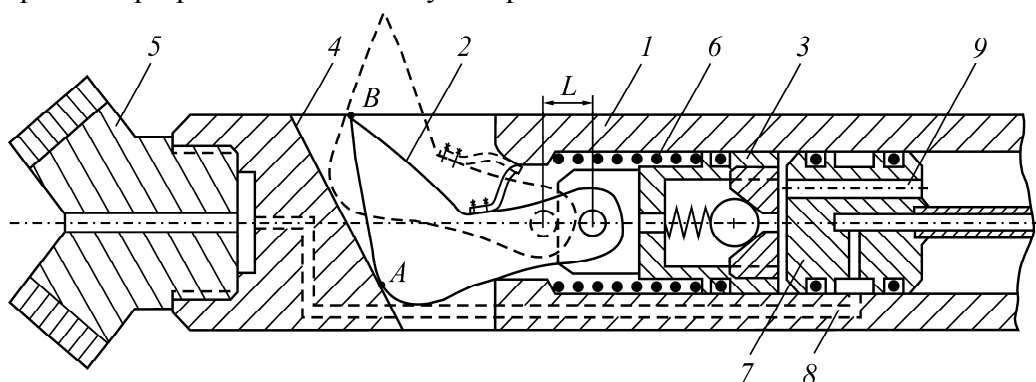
Схема комбинированного устройства КУ-1: 1 — корпус; 2 — режущий орган; 3 — поршень; 4 — направляющий уклон; 5 — резец; 6 — пружина возврата; 7 — запорный поршень; 8, 9 — каналы подвода рабочей жидкости; А — точка опоры режущего органа о направляющий уклон; В — носик режущего органа
